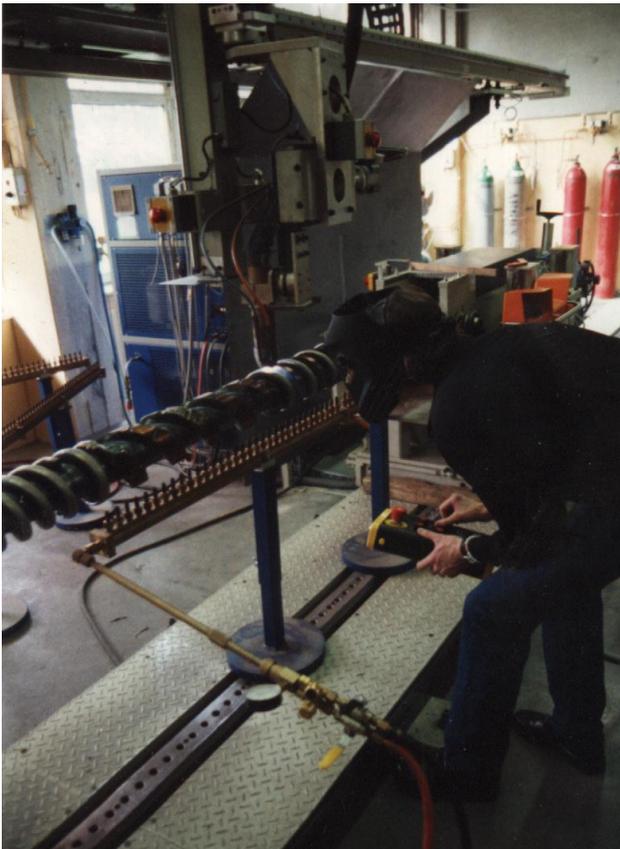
Prozessbeobachtung und Optimierung beim Auftragschweißen mit Robotern
